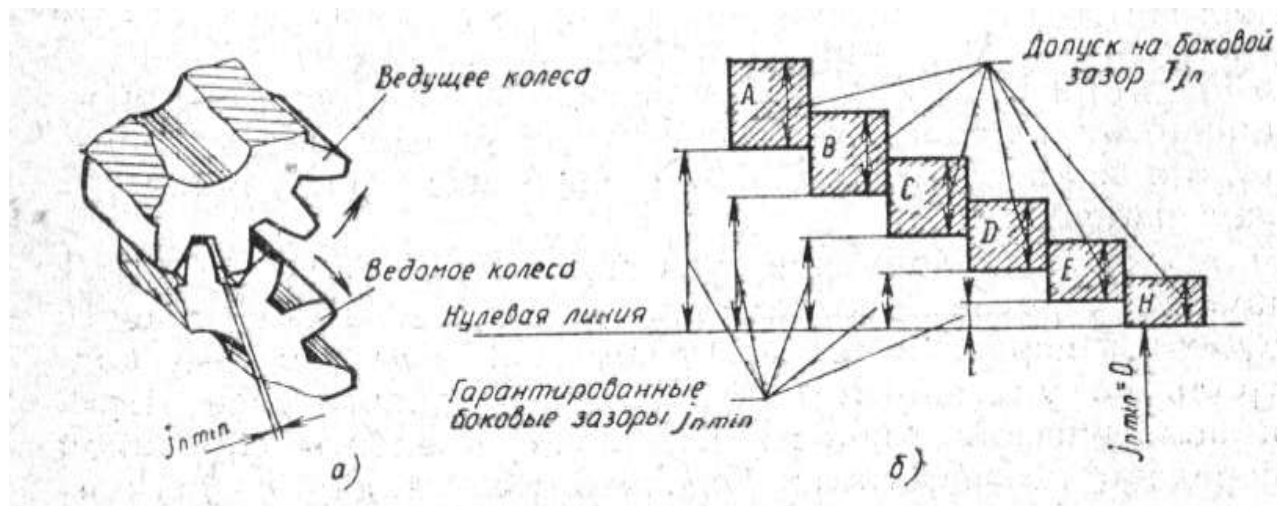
Боковой зазор зубчатого зацепления, виды сопряжений и допуски T_{jn} на боковой зазор
